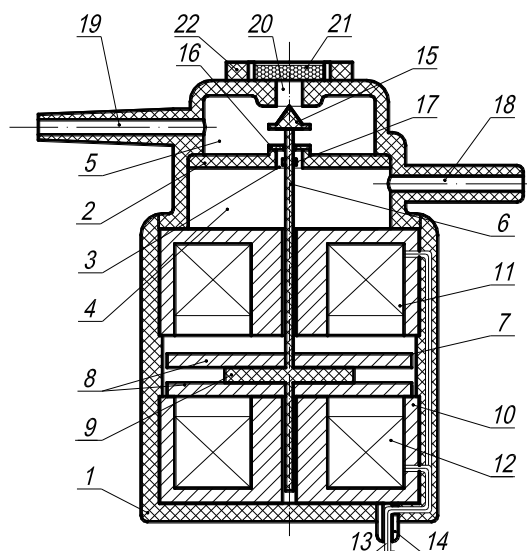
Пульсатор доильного аппарата на основе линейного электродвигателя: 1 – корпус; 2 – перегородка; 3 – отверстие; 4 – камера постоянного вакуума; 5 – камера переменного вакуума; 6 – шток; 7 – якорь; 8 – диски магнитопроводящие; 9 – немагнитная прослойка; 10 – магнитопроводы; 11, 12 – катушки намагничивающие; 13 – выводы катушек; 14 – ввод кабельный; 15 – клапан конусный; 16 – клапан тарельчатый; 17 – упор; 18 – патрубок постоянного вакуума; 19 – патрубок переменного вакуума; 20 – атмосферный канал; 21 – фильтр; 22 – крышка.
